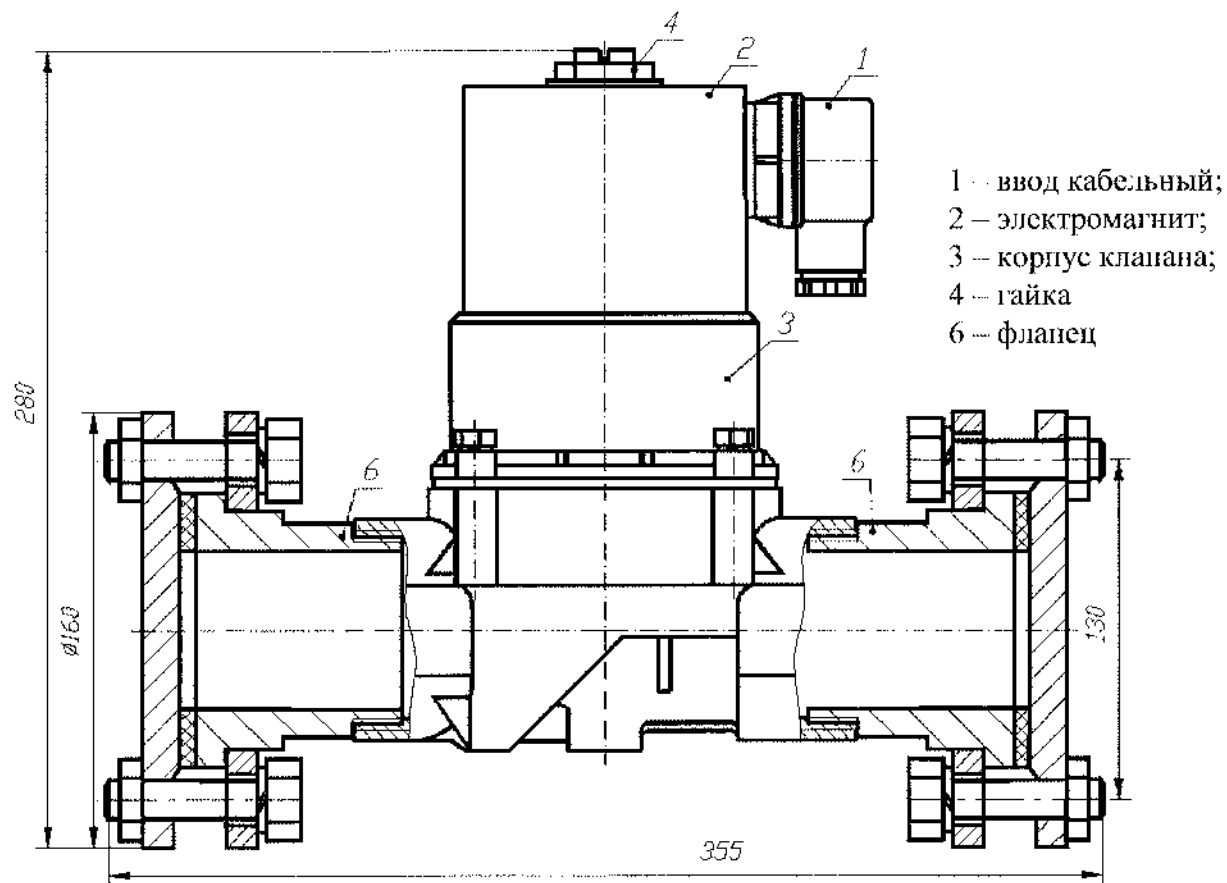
Габаритные и установочные размеры клапана КГЭЗ-65
